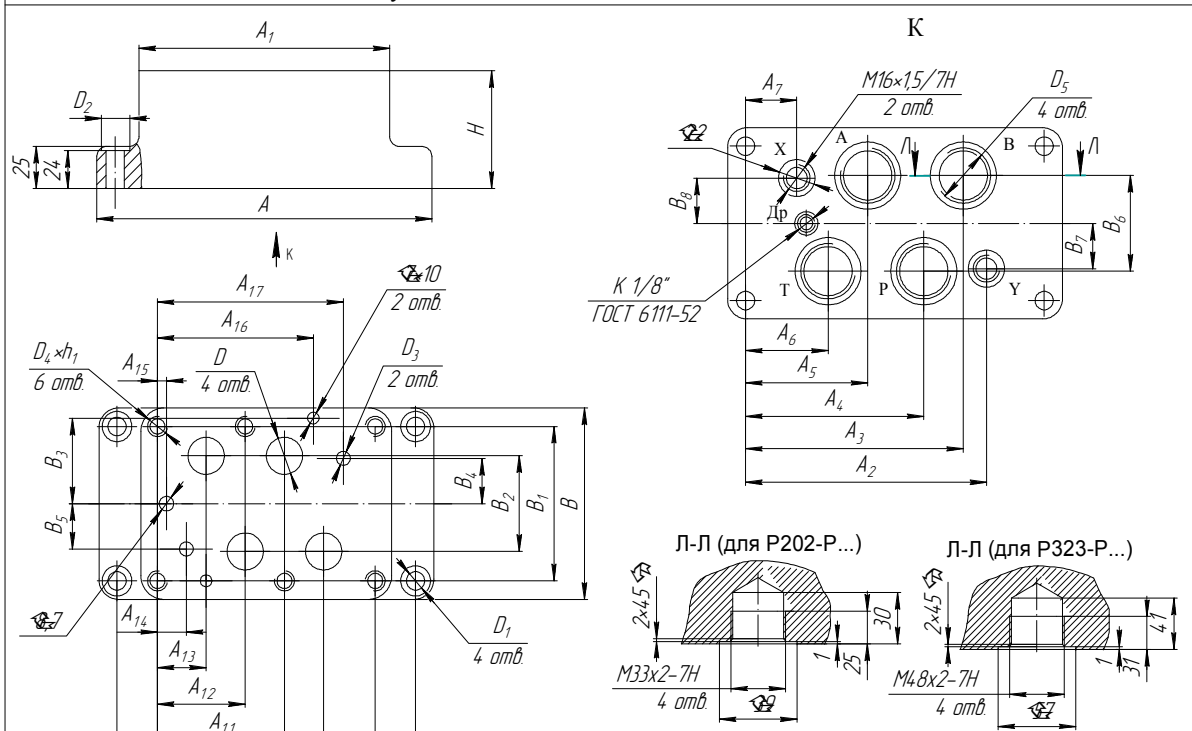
Габаритные и присоединительные размеры присоединительных плит.
